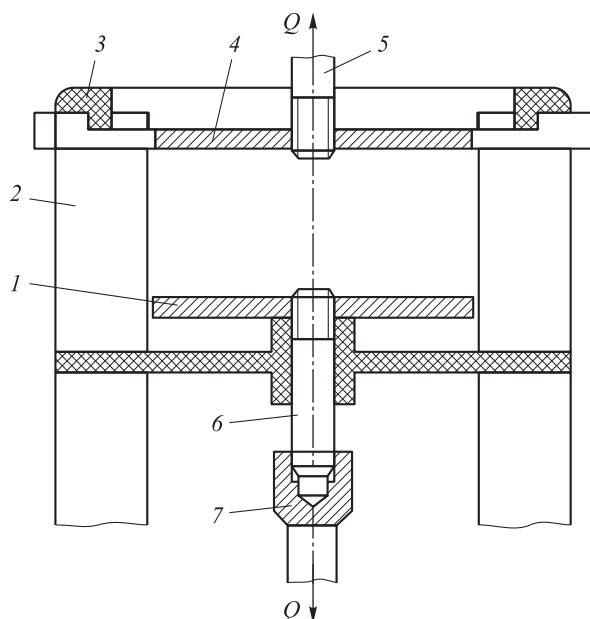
Схема испытания на прочность сварного соединения накладки с лопастями колеса вентилятора
